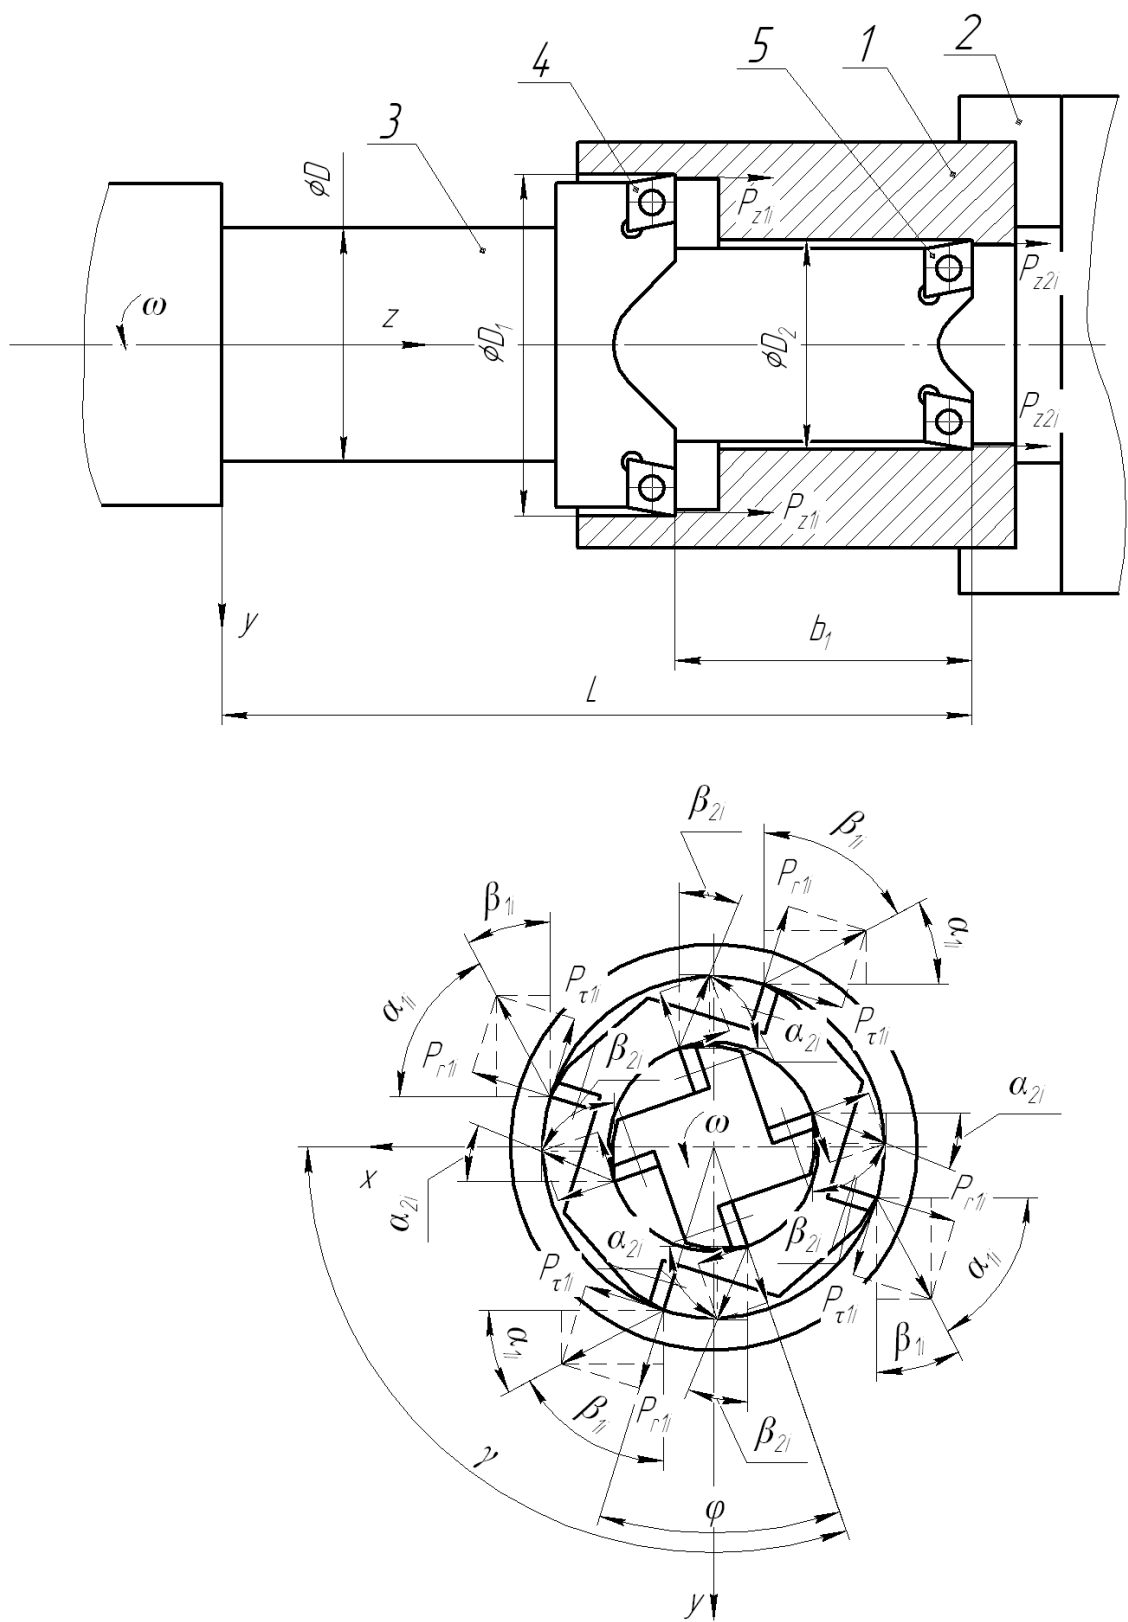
Розрахункова схема розточування ступінчастого отвору для дослідження величини деформації розточної оправки: 1 - заготовка із попередньо обробленим отвором; 2 - затискний пристрій; 3 – ступінчаста оправка; 4, 5 - твёрдосплавні різальні пластини
